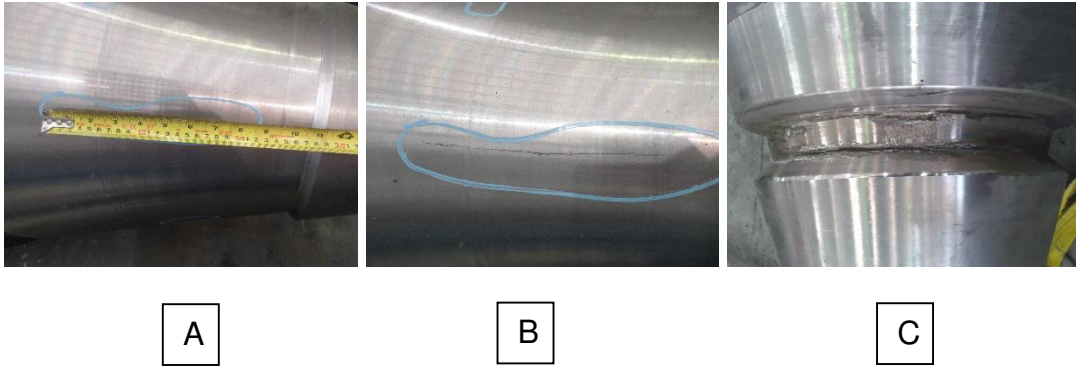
Zona de contacto en herramientas, A.- grietas después de maquinado en axiales, B imagen sin escala de la grieta superficial, C.- defecto de abrasión en axiales.
